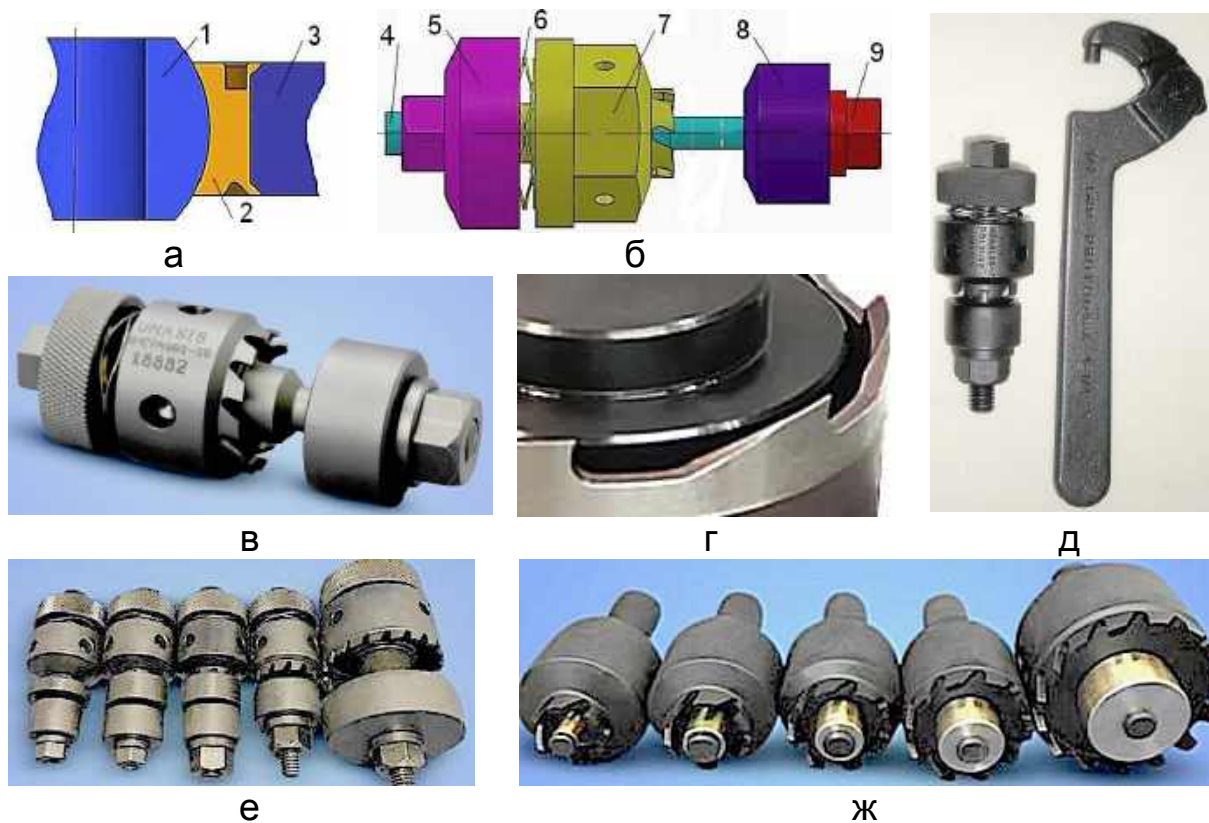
Надрізання зовнішнього кільця підшипників ковзання з V-подібним пазом: 1 – кільце внутрішнє; 2 – кільце зовнішнє; 3 – деталь; 4 – штир; 5 – корпус; 6 – пружина тарілчаста; 7 – державка; 8 – опора; 9 – гайка
